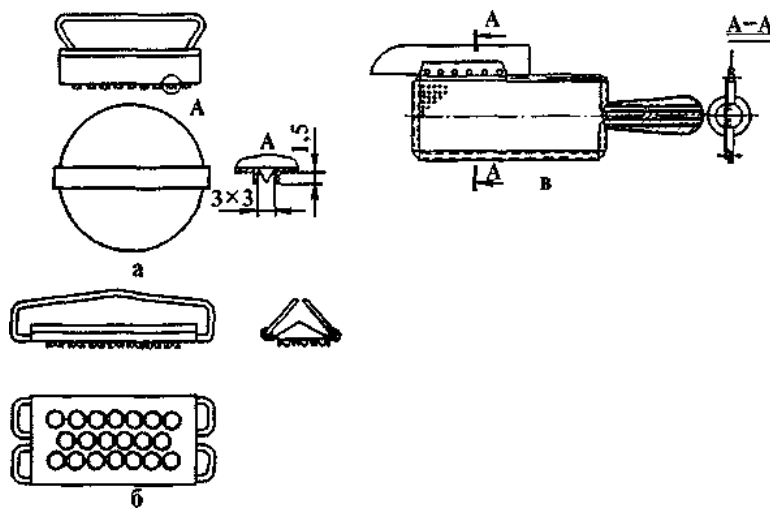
Інструменти з абразивною поверхнею для зняття луски:
